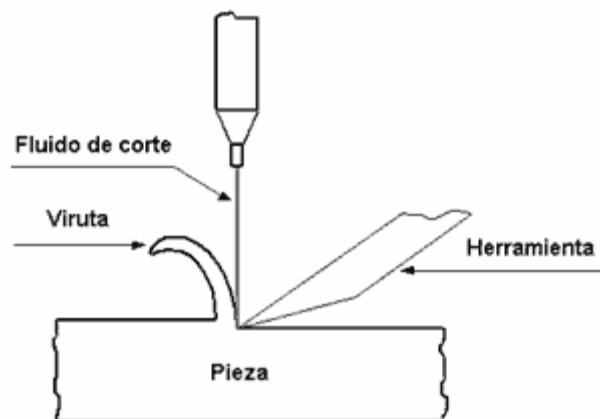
Mecánica del proceso de maquinado del tipo de viruta.
